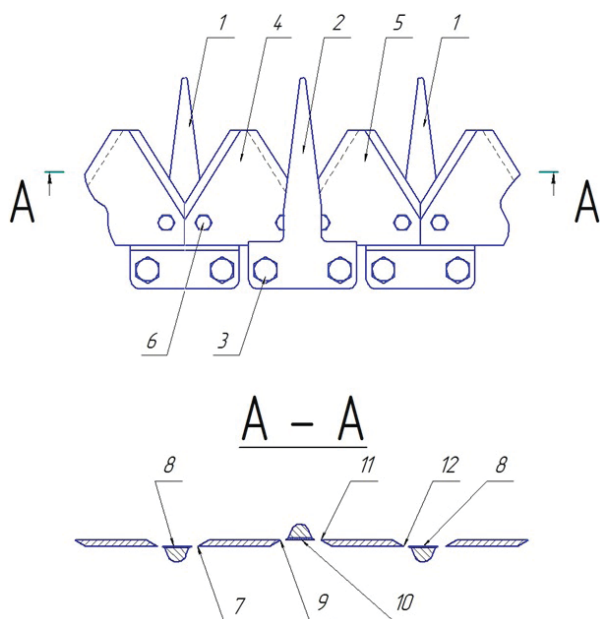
Схема режущего аппарата уборочной машины с пальцами открытого типа:
